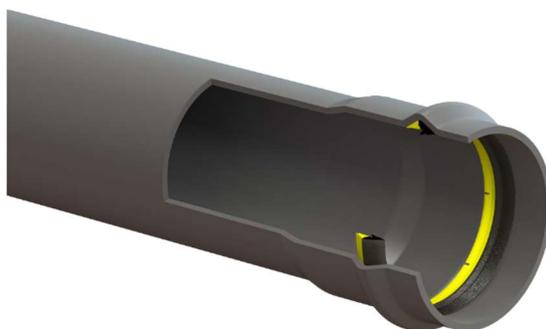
Труба из НПВХ напорная с усиленным уплотнительным кольцом
